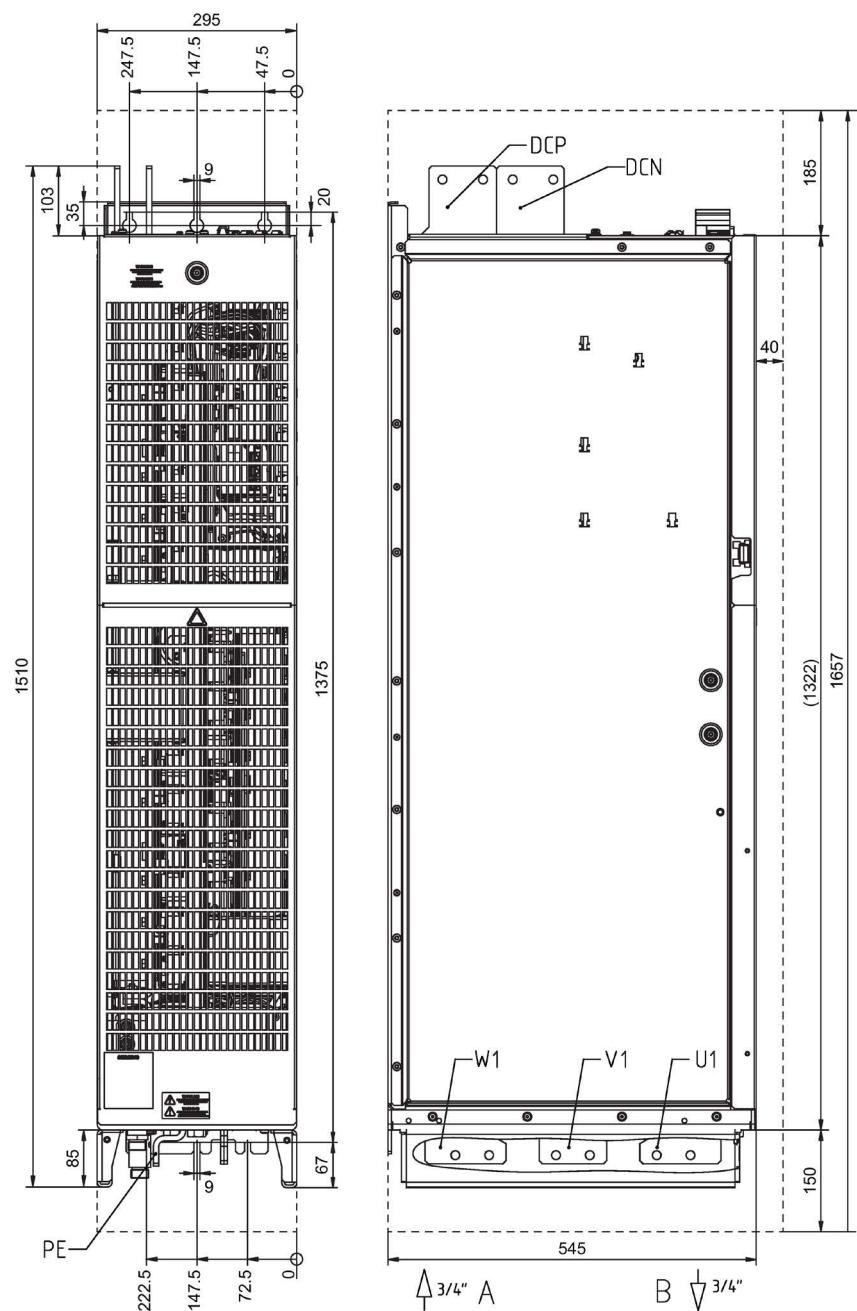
JXL 型调节型电源模块的外形尺寸图，订货号 6SL3335-7TG41-3AA8。正视图和侧视图
